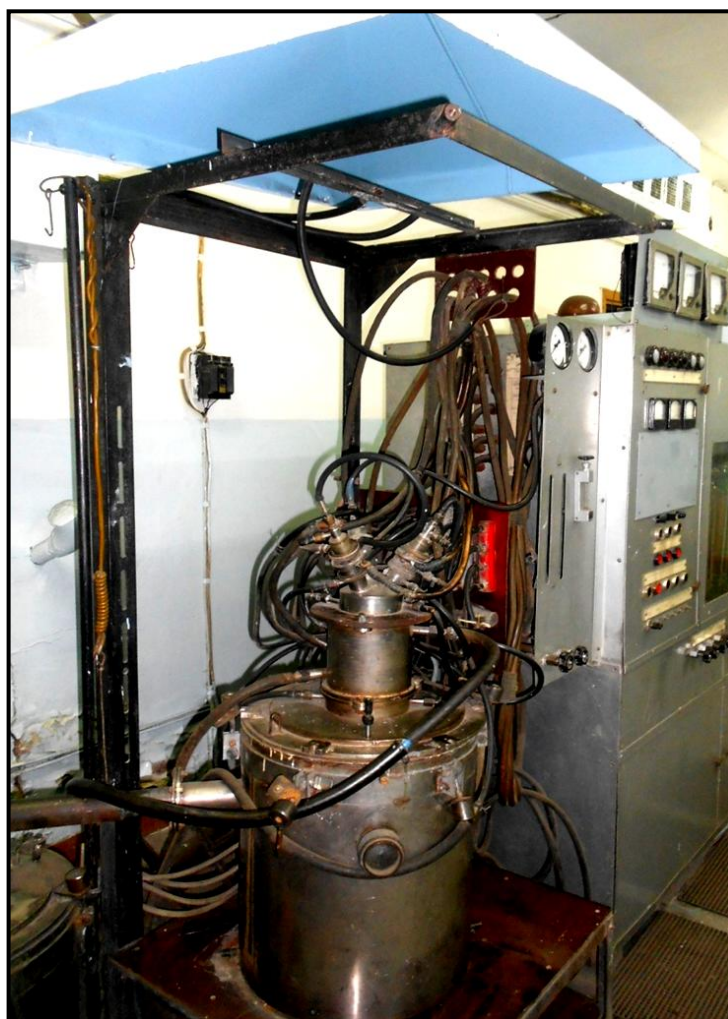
Промышленный плазмометаллургический комплекс
